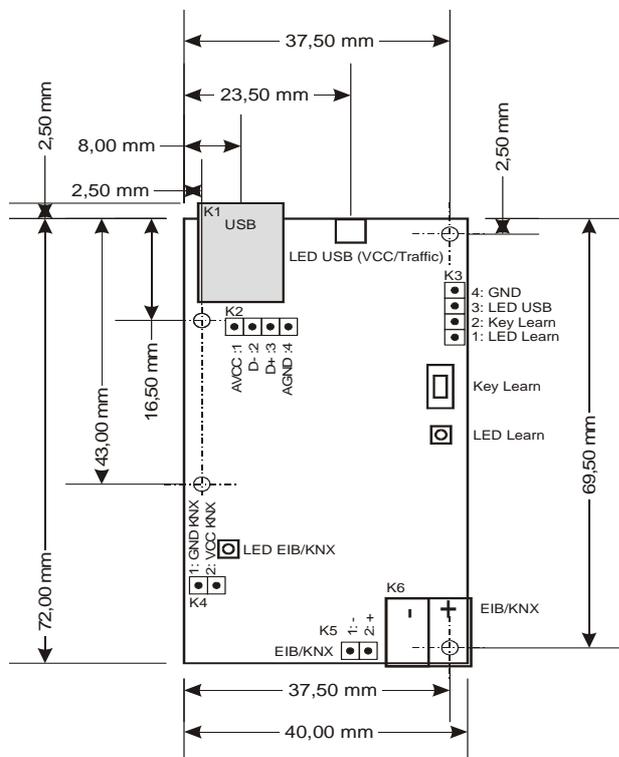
Lageplan Bohrungen, Belegung Anschlüsse
